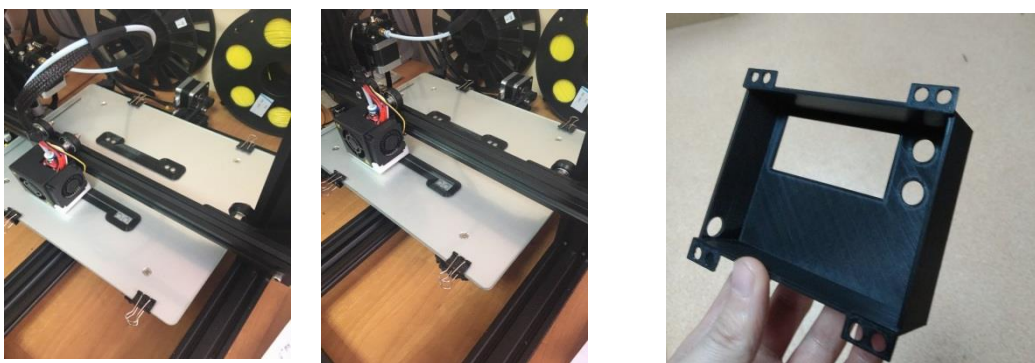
«Корпус, распечатанный на 3D принтере»
